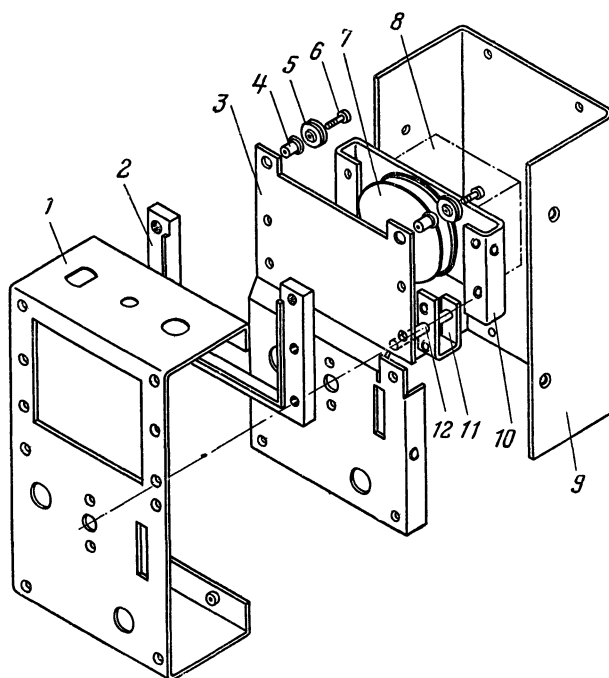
Конструкция корпуса генератора и устройство верньерно-шкального механизма.
